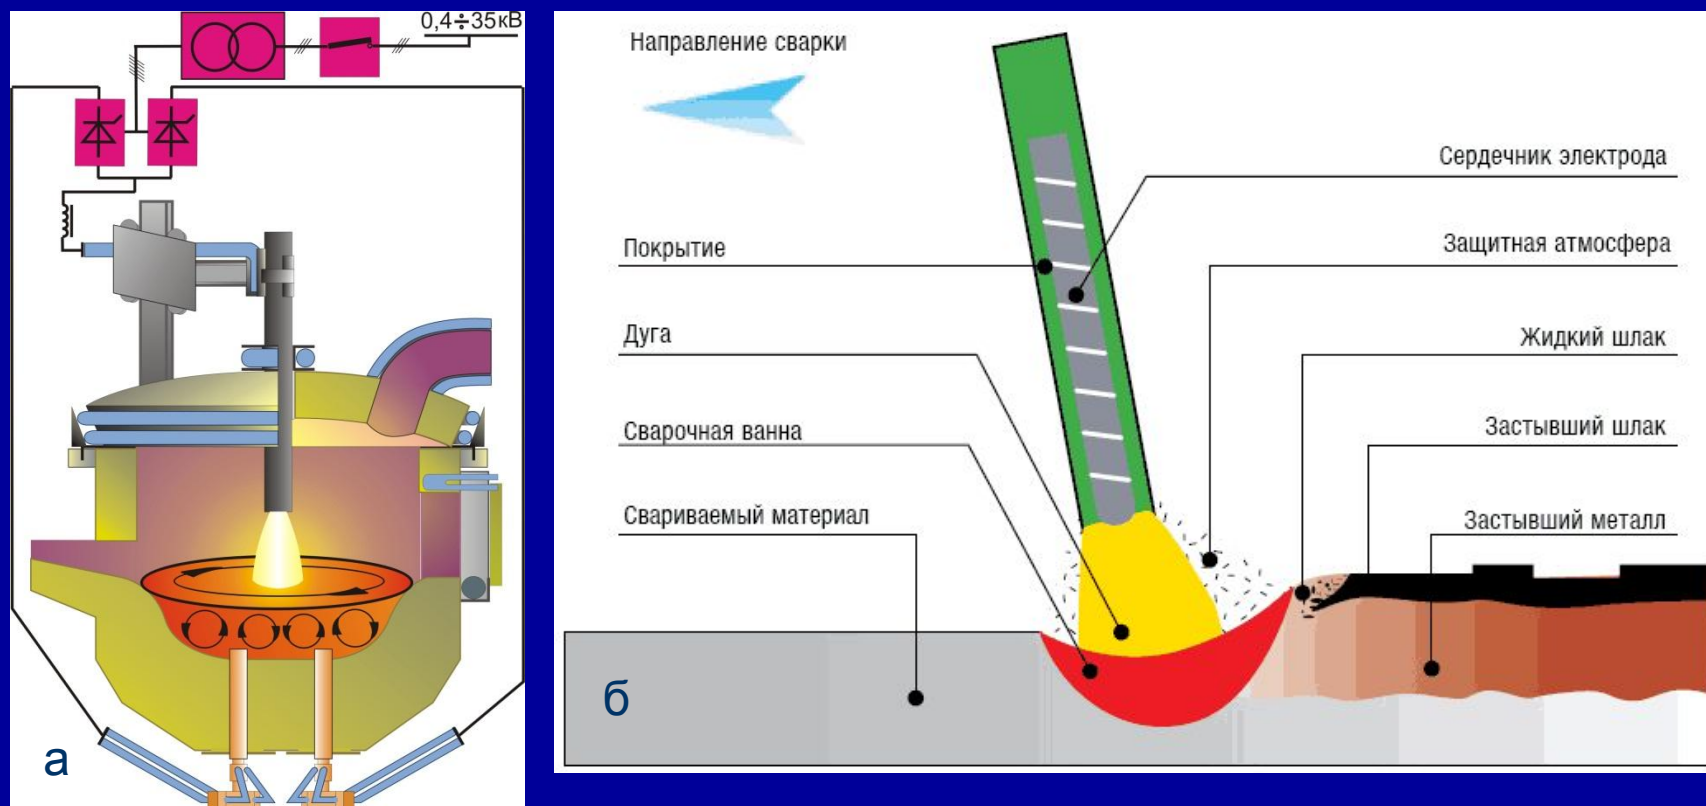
Дуговой нагрев: а) дуговая печь; б) дуговая сварка
